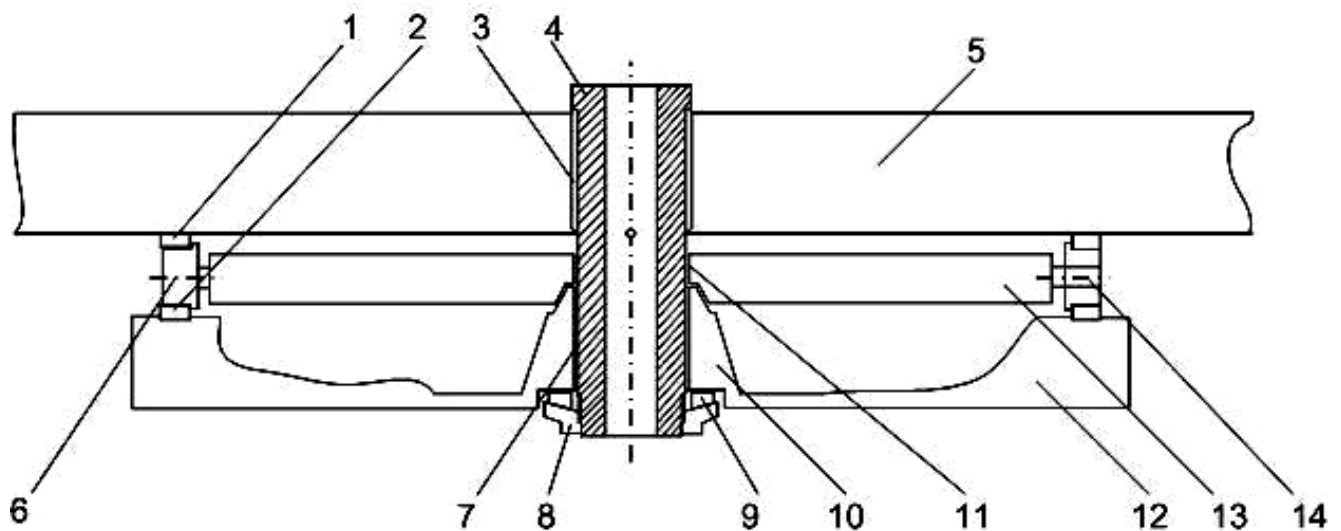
Схема общей конструкции опорно-поворотного устройства экскаватора-мехлопаты
